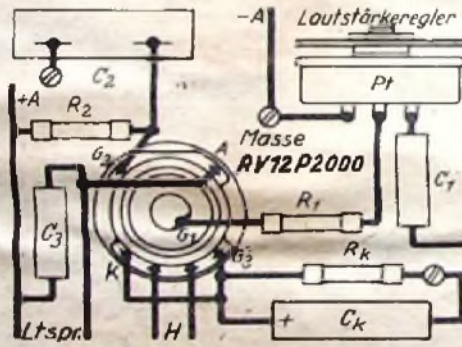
Verdrahtungsplan einer Endstufe mit RV 12 P 2000
